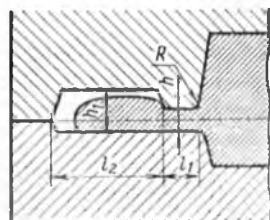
Конструкция облойной канавки молотового штампа:
